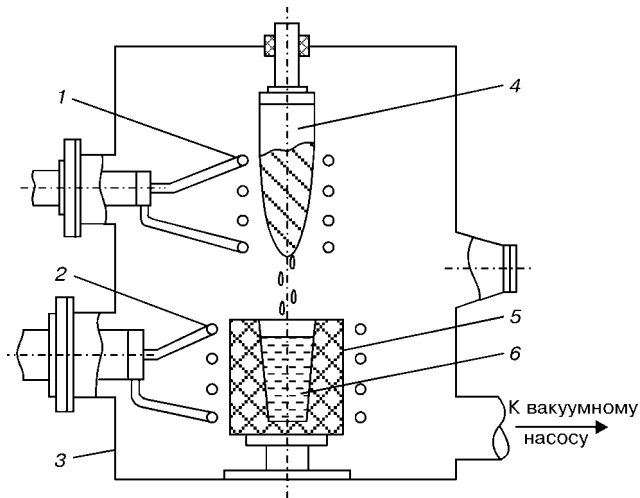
Схема установки для индукционного переплава расходуемой заготовки и получения отливки в литейной изложнице [2]: 1 — верхний индуктор; 2 — нижний индуктор; 3 — плавильная камера; 4 — расходуемая заготовка; 5 — литейная форма; 6 — жидкий металл
